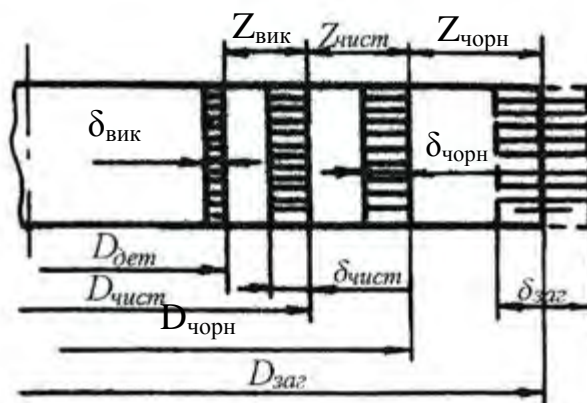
Схема розташування припусків і допусків при багаторазовому обробленні зовнішньої поверхні обертання
